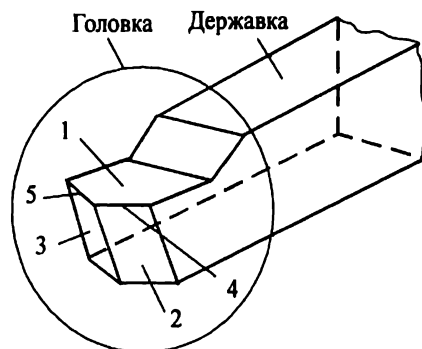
Конструктивные элементы токарного резца: 1 – передняя поверхность; 2 – главная задняя поверхность; 3 – вспомогательная задняя поверхность; 4 – главная режущая кромка; 5 – вспомогательная режущая кромка
